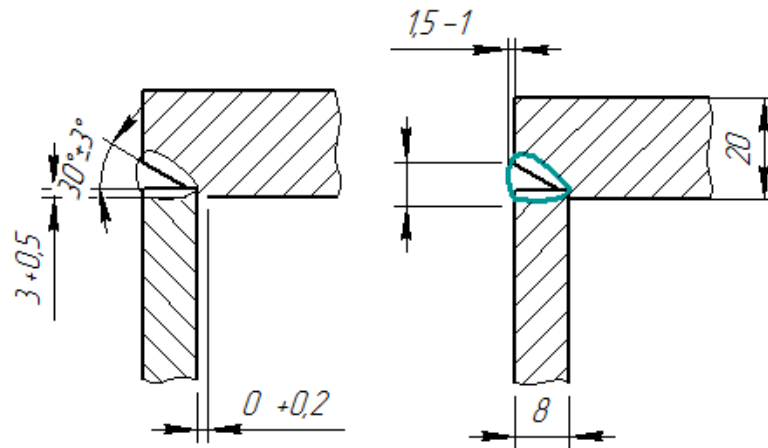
Форма и размеры сварного соединения II.
